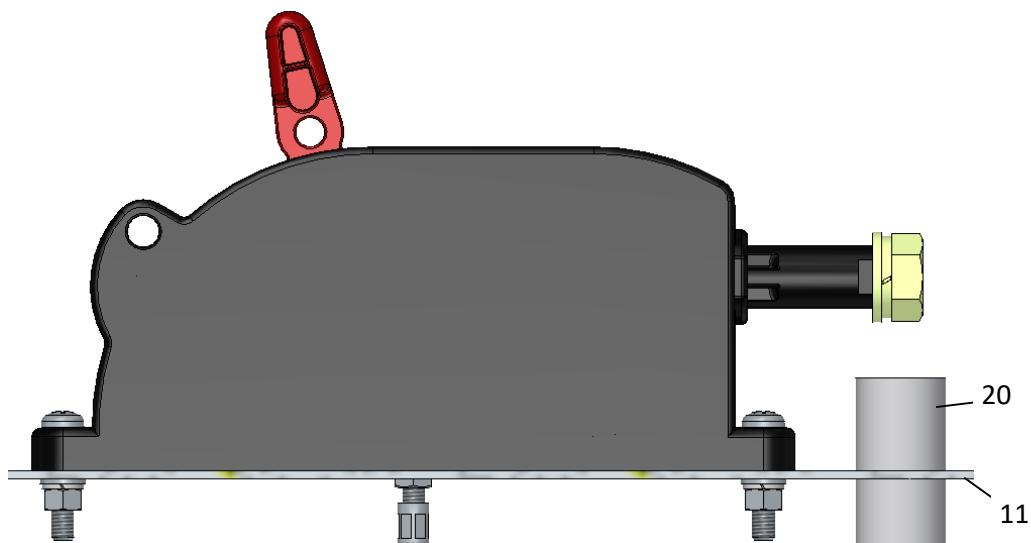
Блокиратор закрывающий доступ к червячному редуктору
